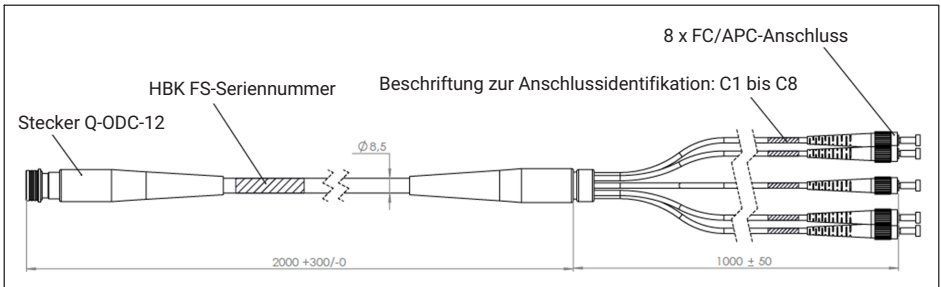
Technische Zeichnung des Anschlusskabels (Abmessungen in mm)
